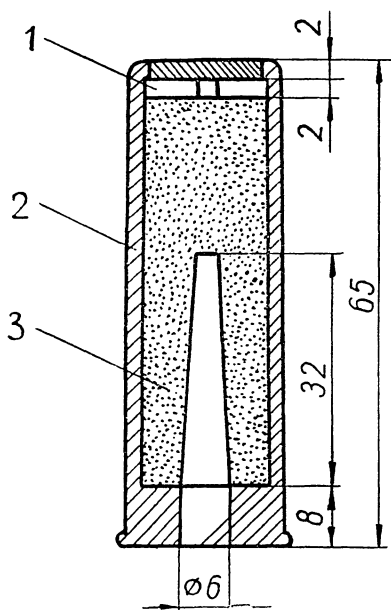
Ракетный заряд: 1 — пыж картонный с отверстием в центре 3 мм; 2 — ракетный патрон; 3 — ракетный заряд.
